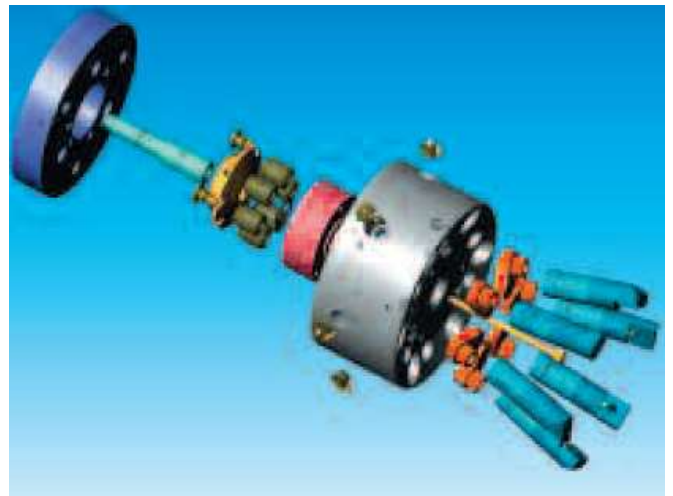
Токарний 6-кулачковий патрон ROTA NCR фірми SCHUNK:
